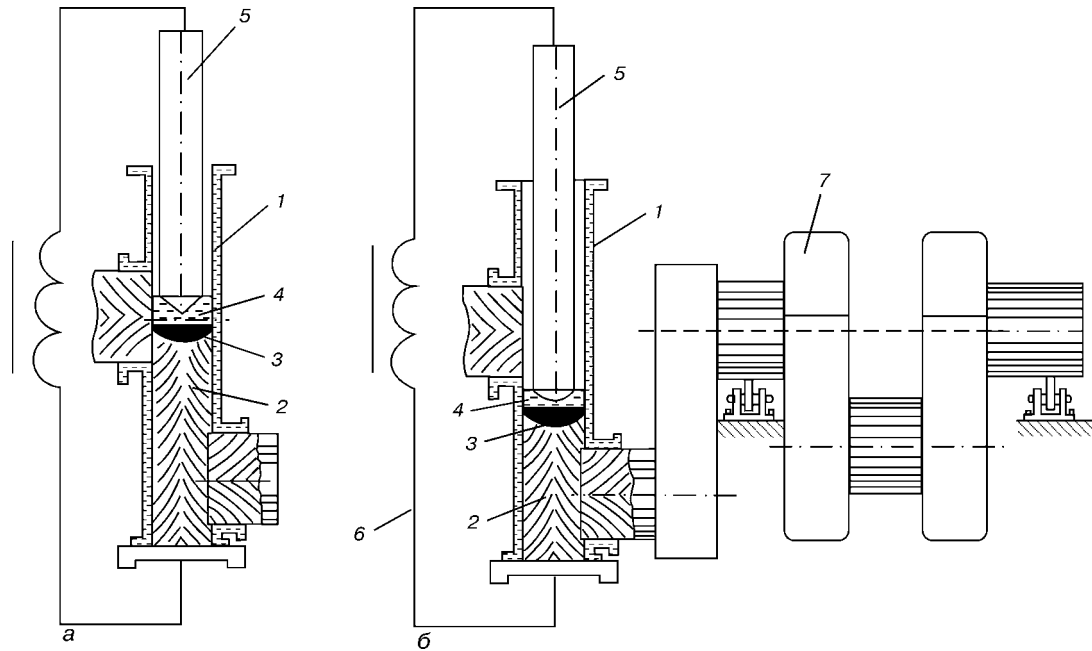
Схема электрошлакового литья коленчатого вала целиком: *а* — выплавка первой щеки с приплавлением щеек; *б* — выплавка коленчатого вала; обозн. 1–6 см. на рис. 1; 7 — коленчатый вал
